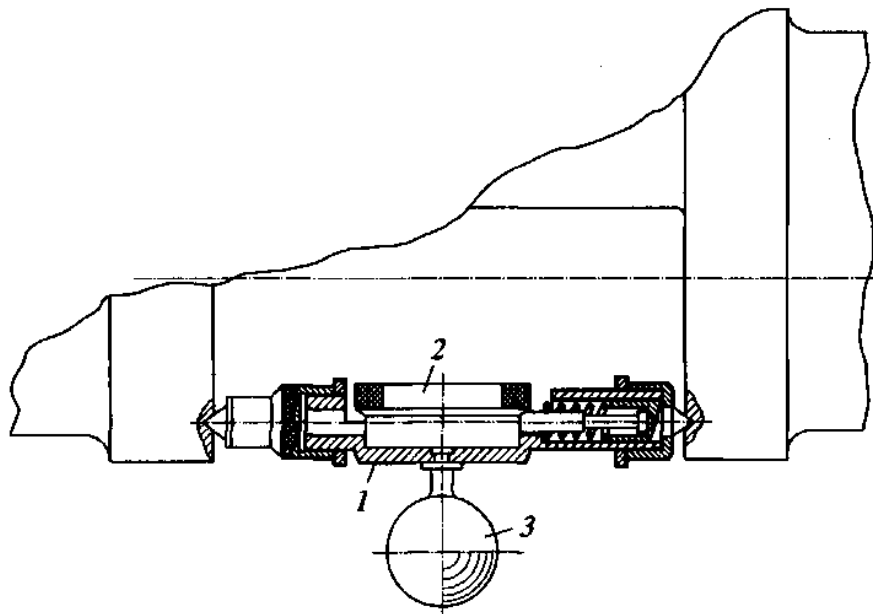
Индикаторное приспособление для измерения расхождения щек шатунной шейки коленчатого вала дизеля:
